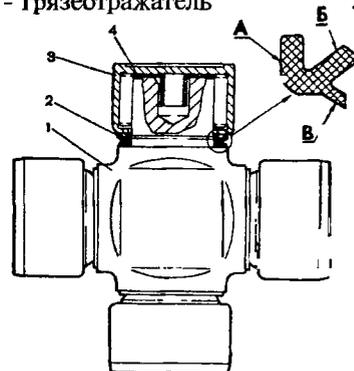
Крестовина карданного шарнира в сборе: 1 - крестовина; 2 - сальник радиально-торцевого уплотнения; 3 - игольчатый подшипник; 4 - торцевая шайба; А, Б, В - уплотнительные поверхности сальника
